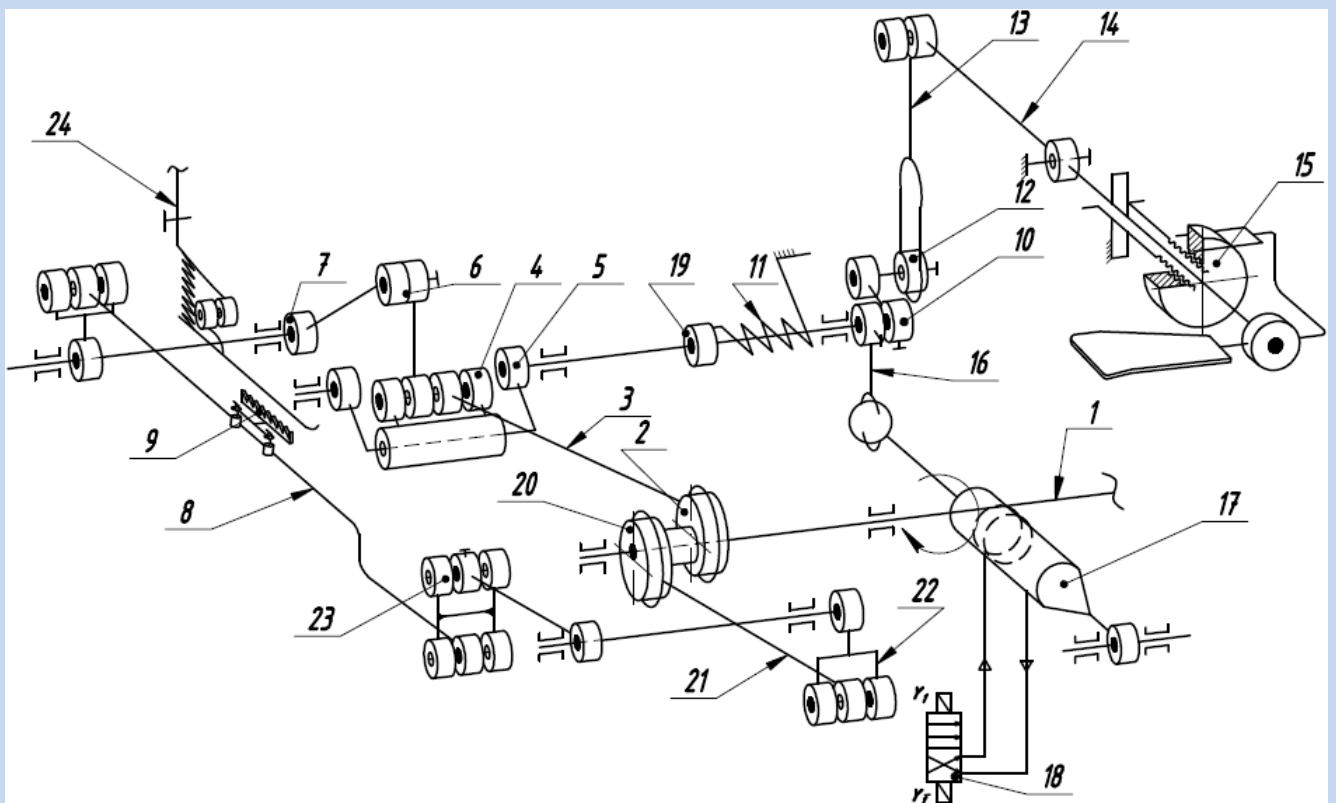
кінематично принципова схема механізму зубчастої рейки
